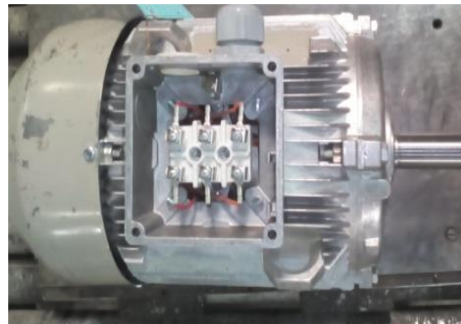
Boîte à bornes et flasque montés sur La carcasse du moteur
